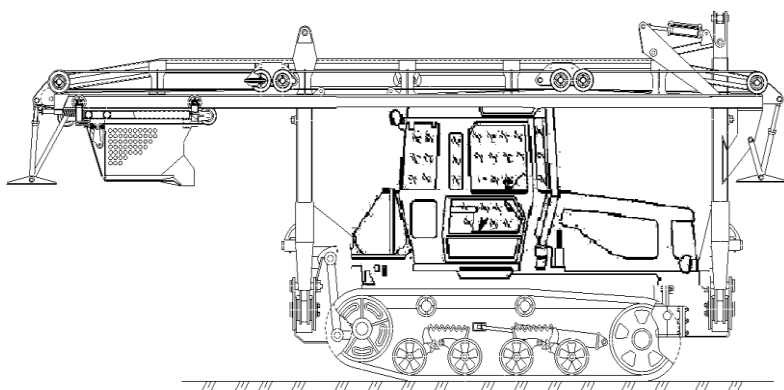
Каналоочиститель РР-303М – вид сбоку на базе трактора ВТГ-90
